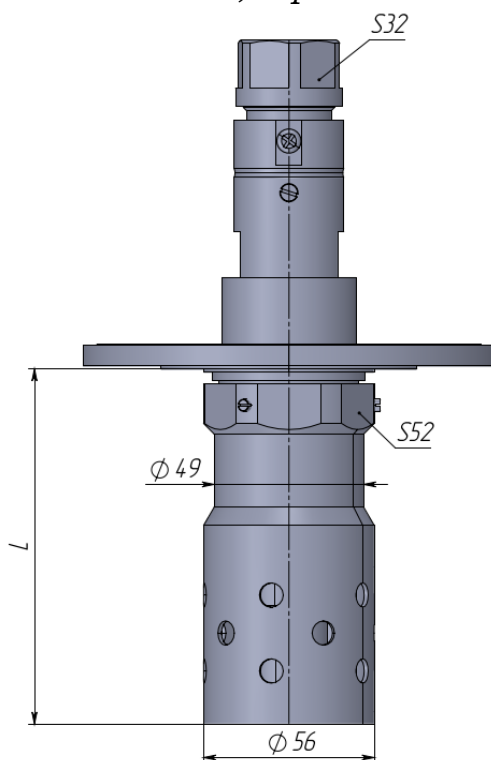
Цилиндрический неизолированный РИС-121-265
